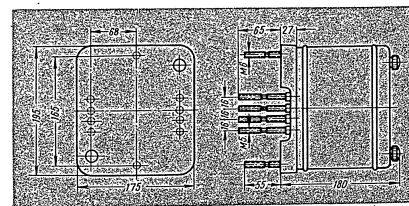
Габаритные и установочные размеры реле типа ЭТ-523/1Д с задним присоединением
